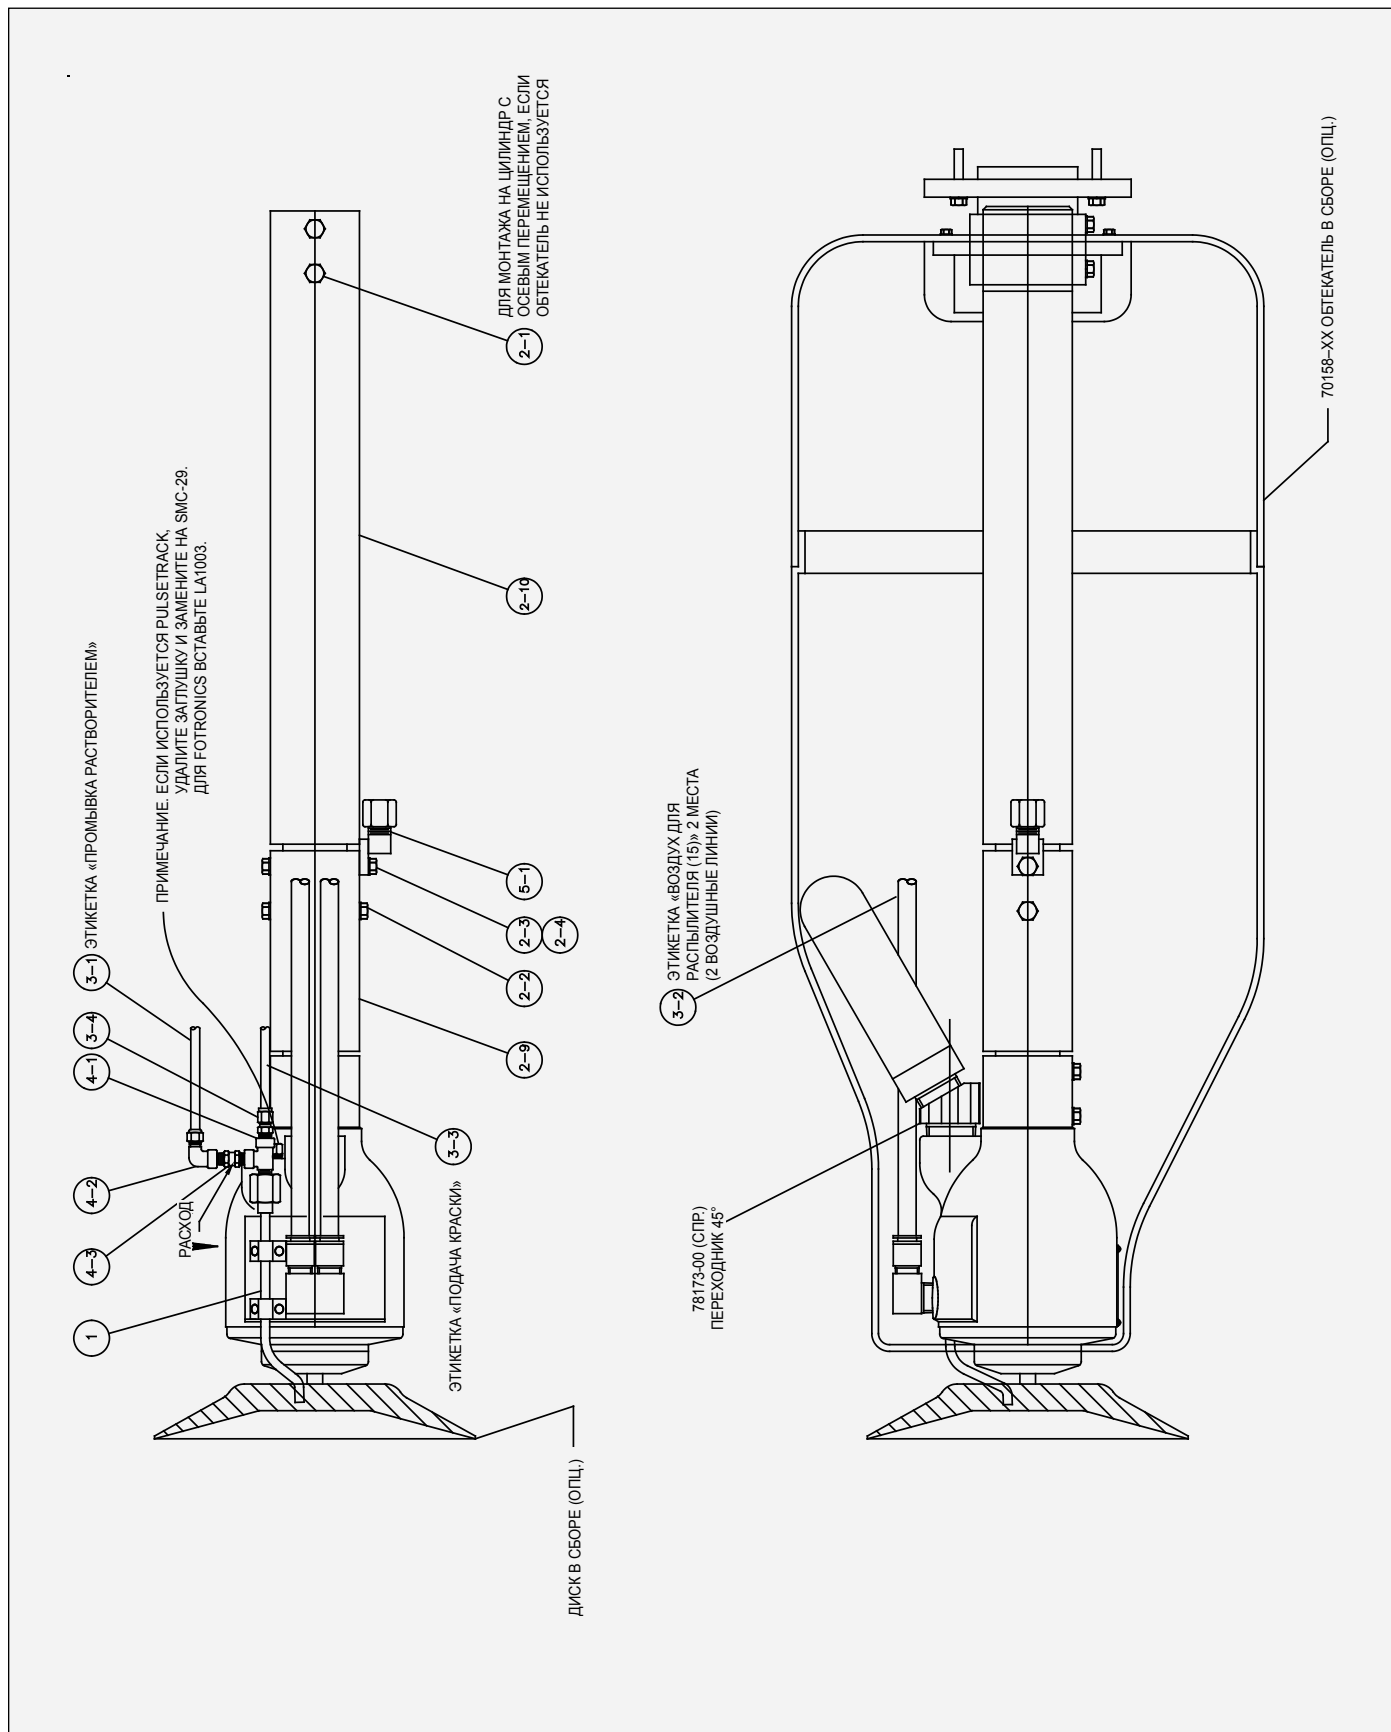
Аппликатор 70990-05 Turbodisk в сборе, без клапанов
